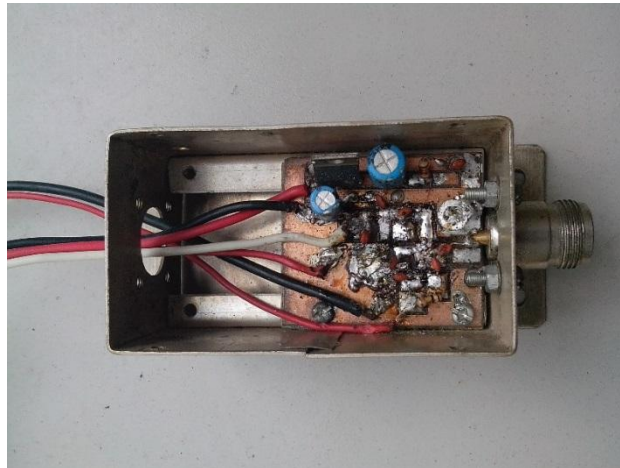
Bố trí PCB thông thường của SPF-3043.
